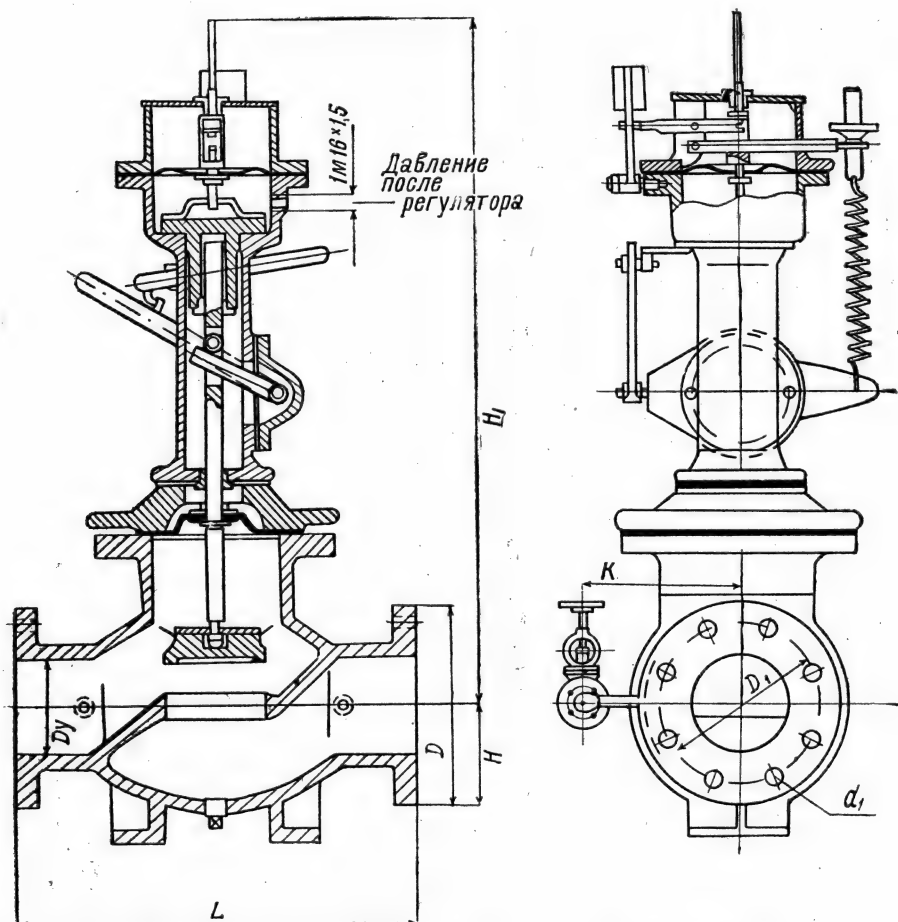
Предохранительный запорный клапан с пружинной нагрузкой для отключения потока при повышении давления газа типа ПК-150, ПК-200 и ПК-300. Конструкция клапанов с пружинной нагрузкой ПК-80 и ПК-100 аналогична рис. 9.35.
